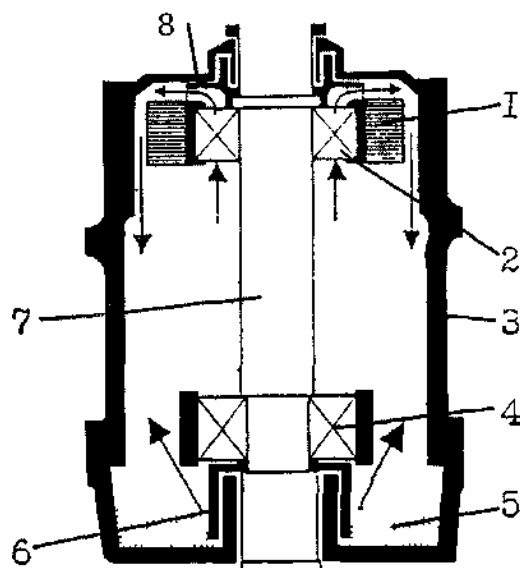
Корпус подшипников вертикального вала. 1-резиновый амортизатор; 2-верхний подшипник; 3-корпус подшипников; 4-нижний подшипник; 5-картер масла; 6-масляный насос; 7-вертикальный вал; 8-вентилятор.
